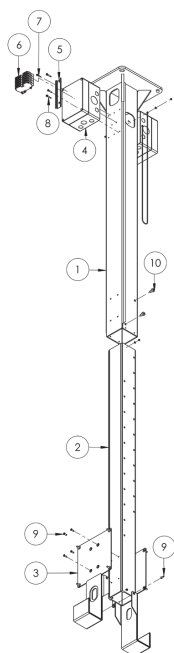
Explosionszeichnung des Deckenmontagesatzes
